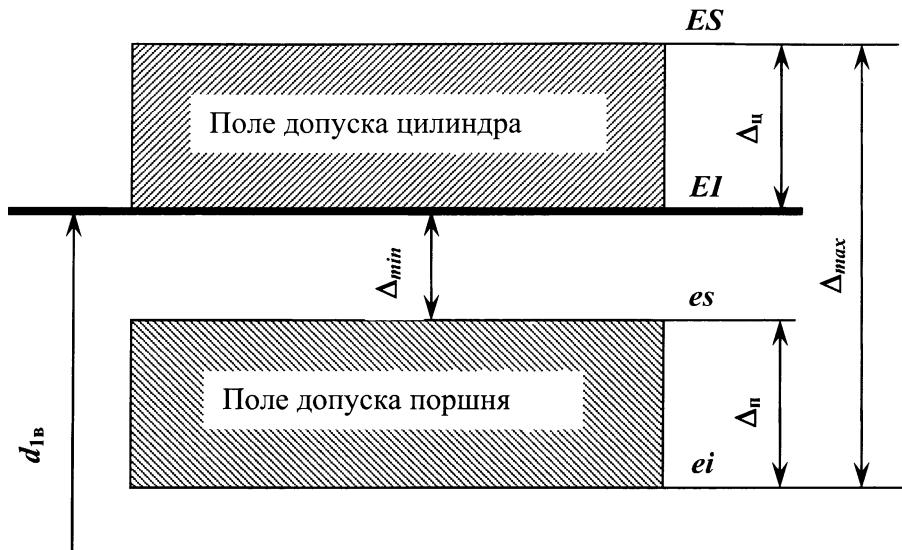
Схема расположения полей допусков поршня и цилиндра гидростойки
